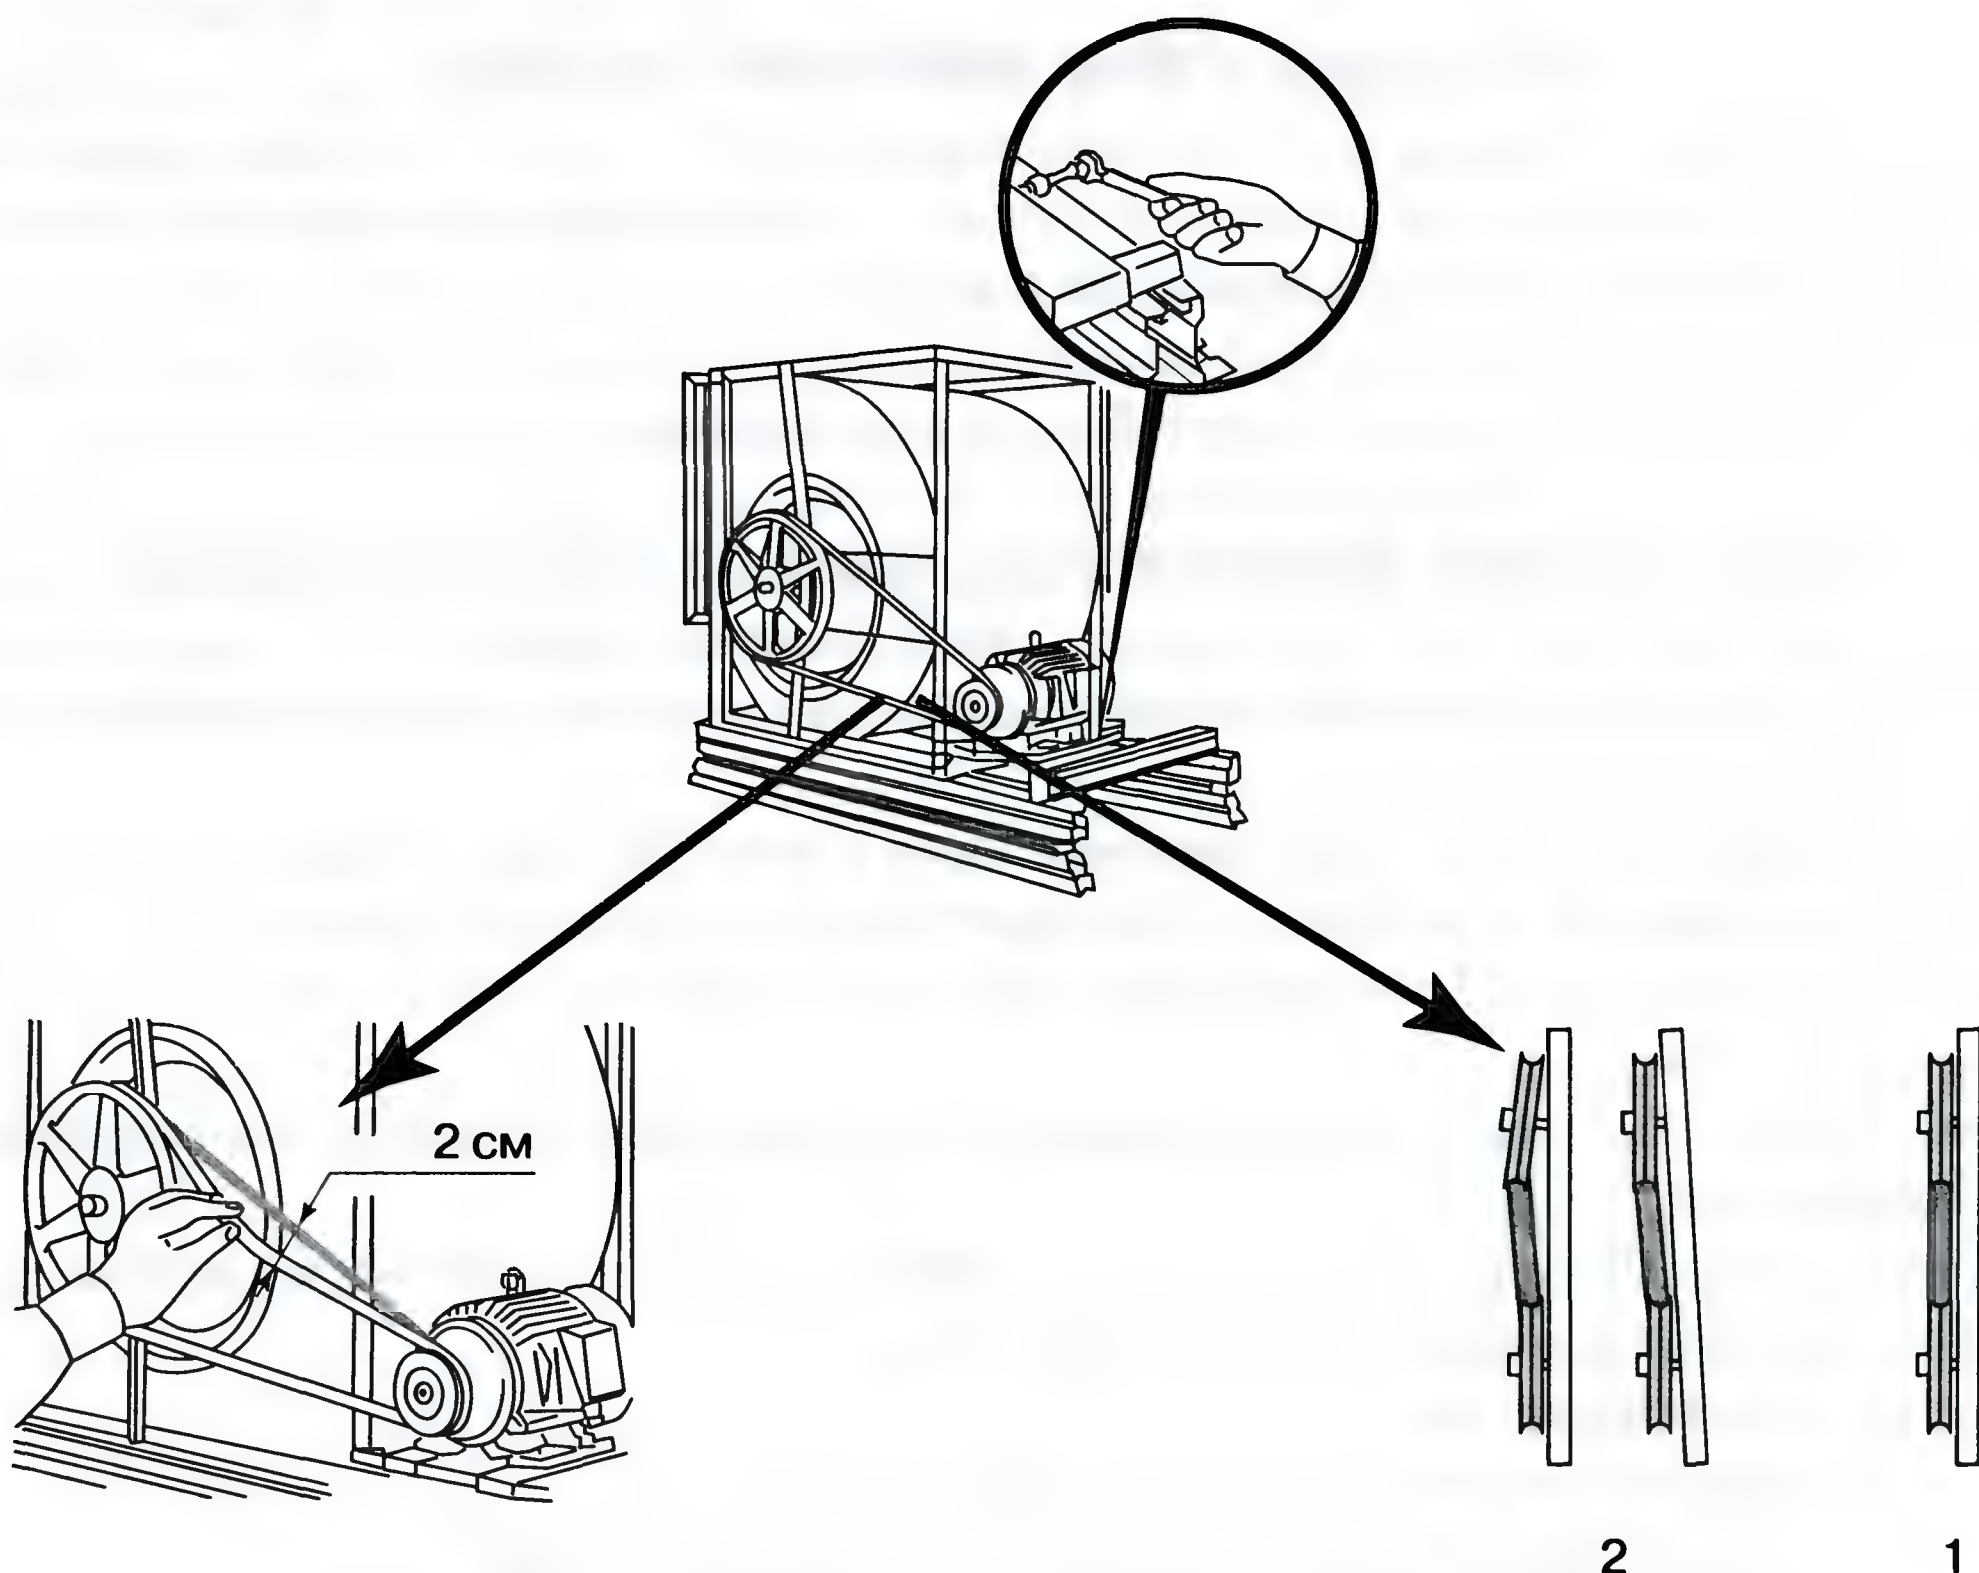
Положение шкивов клино-ременной передачи:
